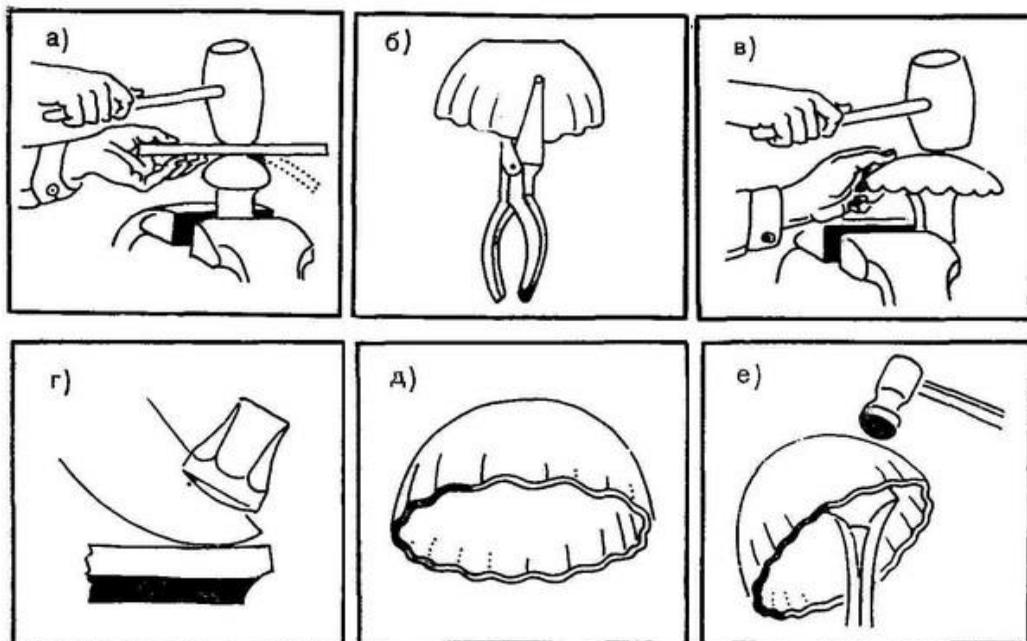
Рабочее положение дифовщика и пример выколотки полушара: а) - выбивание небольшой выпуклости; б) - гофрирование края заготовки; в) - посадка гофров и осадка краев внутрь; г) - выколотка середины заготовки на плите; д) - заготовка с вторично нанесенными гофраами; е) - проглаживание полушара на круглой стойке молотком-гладильником
